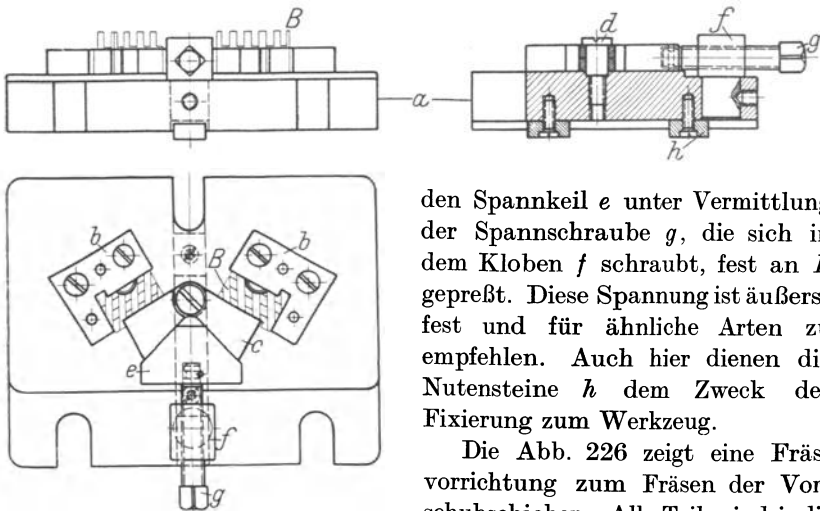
Fräsvorrichtung zum Fräsen der Eingriffe in Spannbacken.
